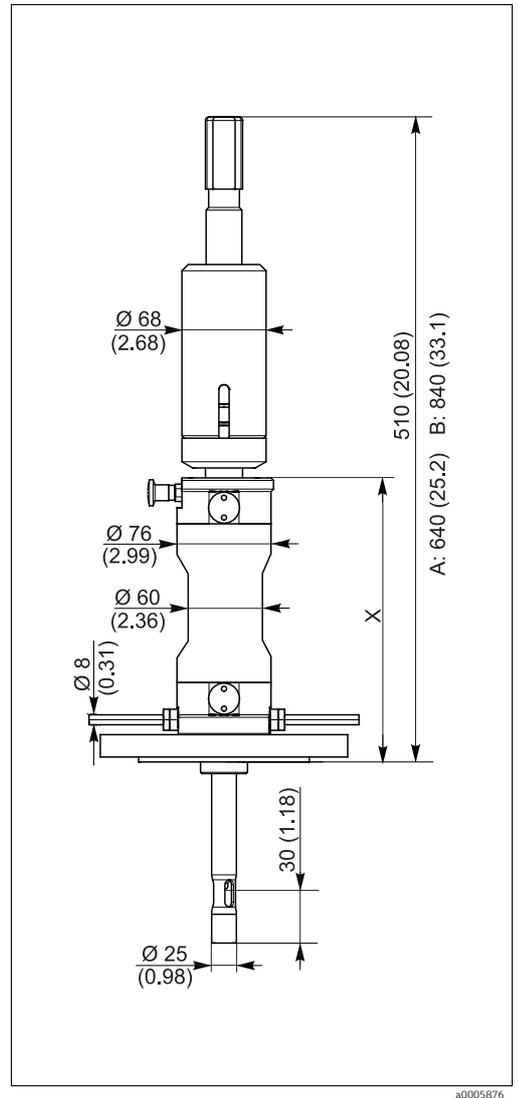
Ausführung: Standard für KCl-Sensoren. Abmessungen in mm (inch)
